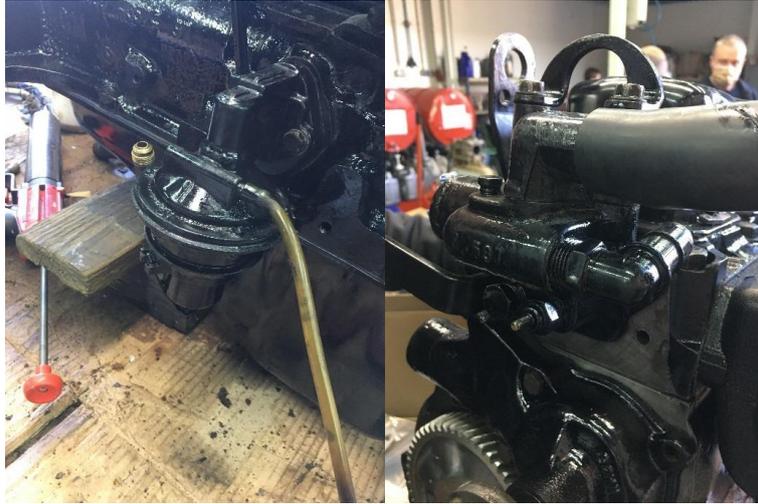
Bomba de combustível e corpo do termostato do motor
